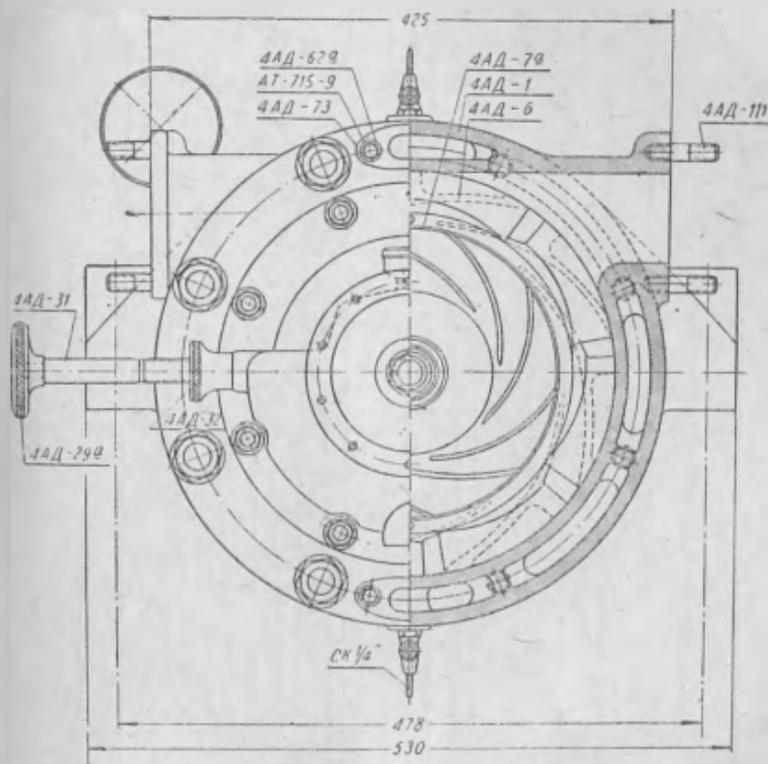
Вид со стороны приводного вала и поперечный разрез центробежного турбонасоса.
